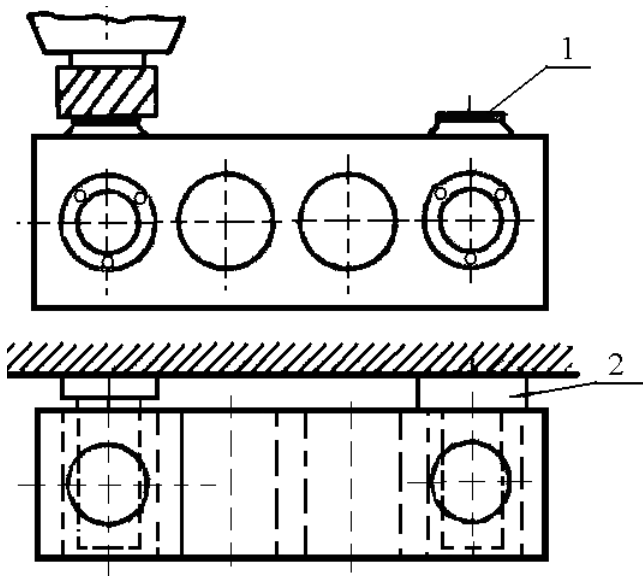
Схема установки корпусной детали на два не обработанных отверстия с параллельными осями
